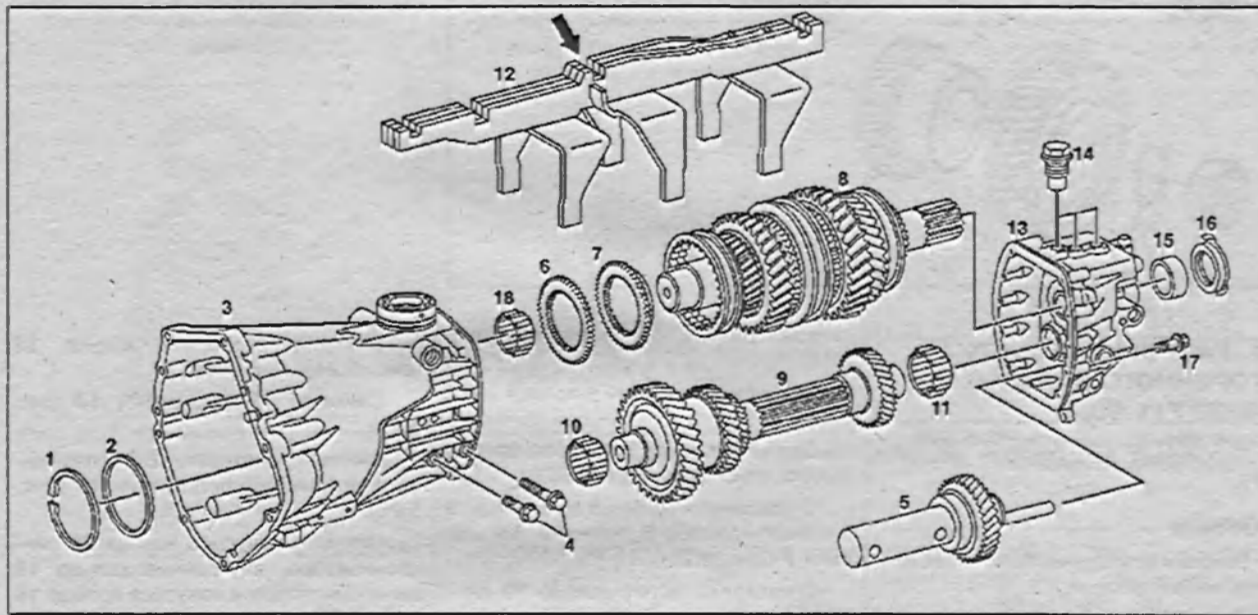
а. Вторичный и промежуточный валы коробки передач 711.603:
